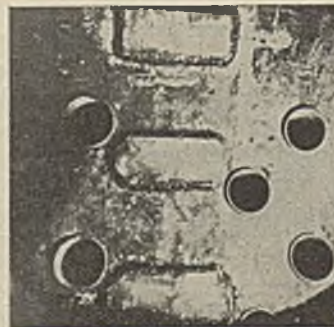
Aufgeschweißte Sicherungslaschen über einer ausgebesserten wassergasschweißten Rundnaht einer Kesseltrommel.
